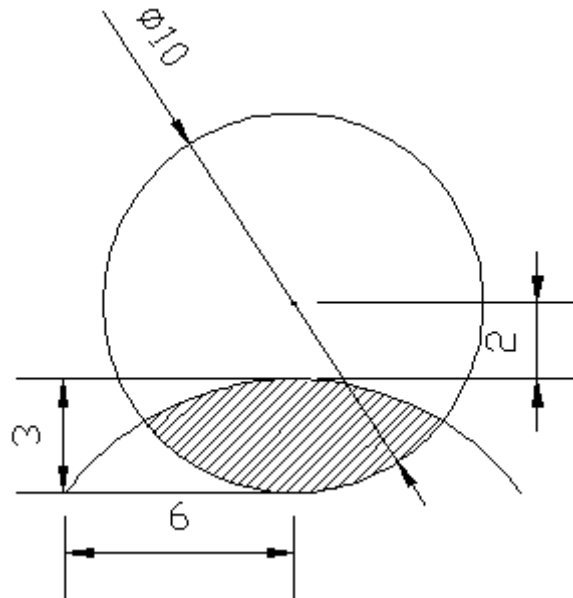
Vista transversal de la sección fisurada para la barra 16
